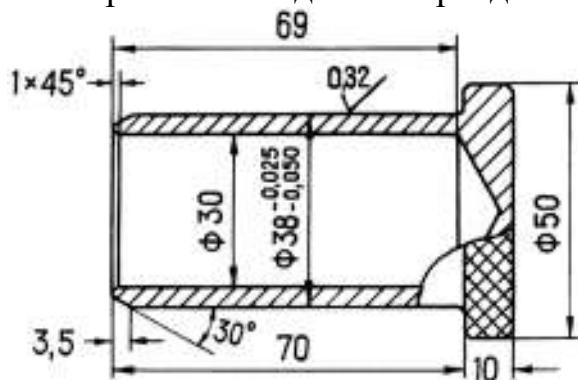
Пробка-заглушка отверстия в удлинителе коробки передач
